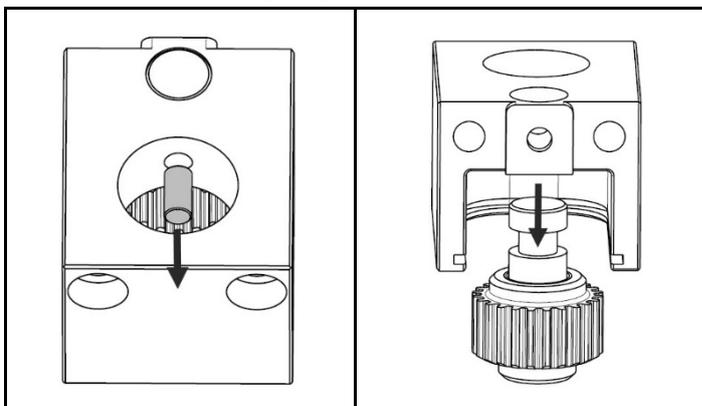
Remova o pino de encaixe seguido pelo conjunto da engrenagem intermediária
